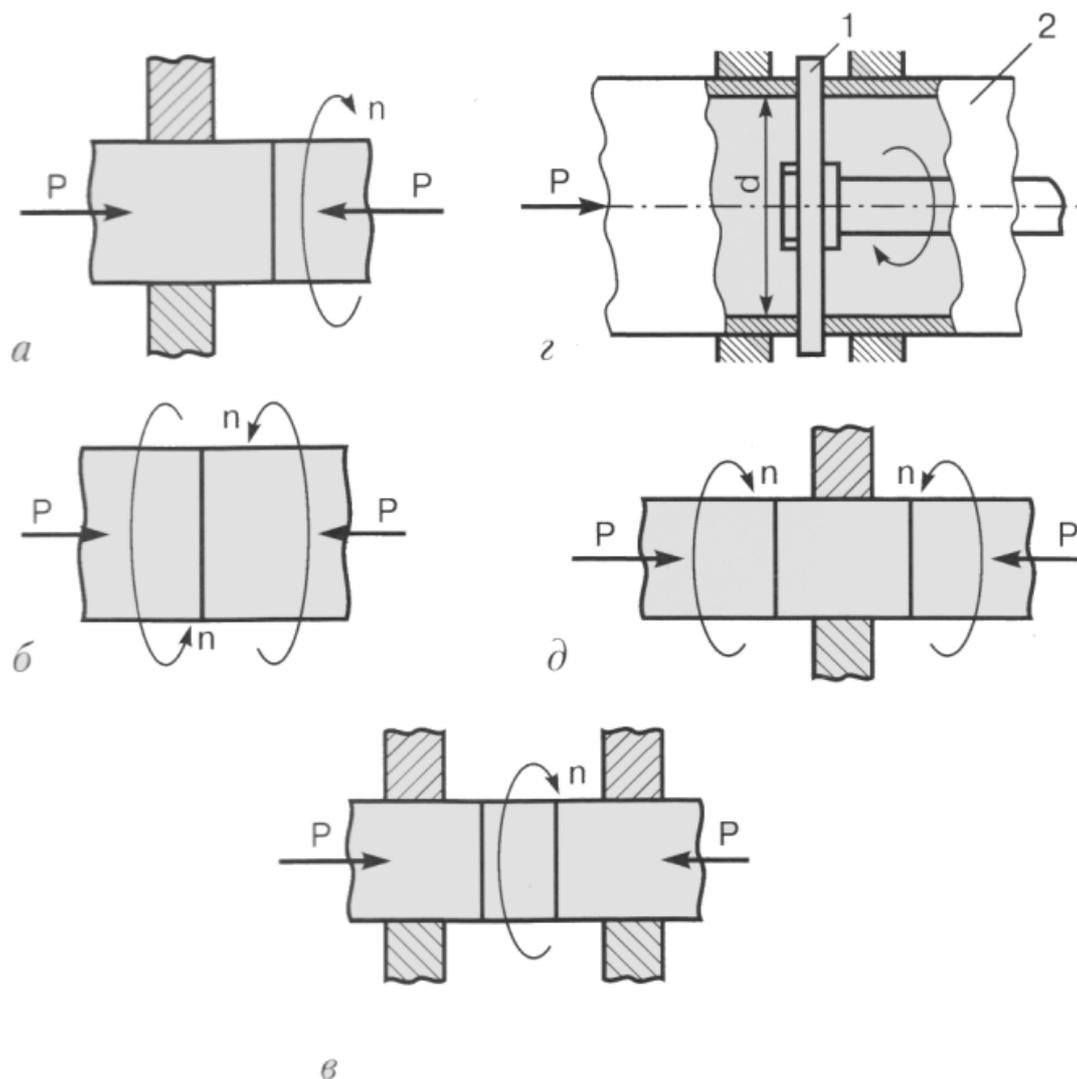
Принципиальные схемы сварки трением:
